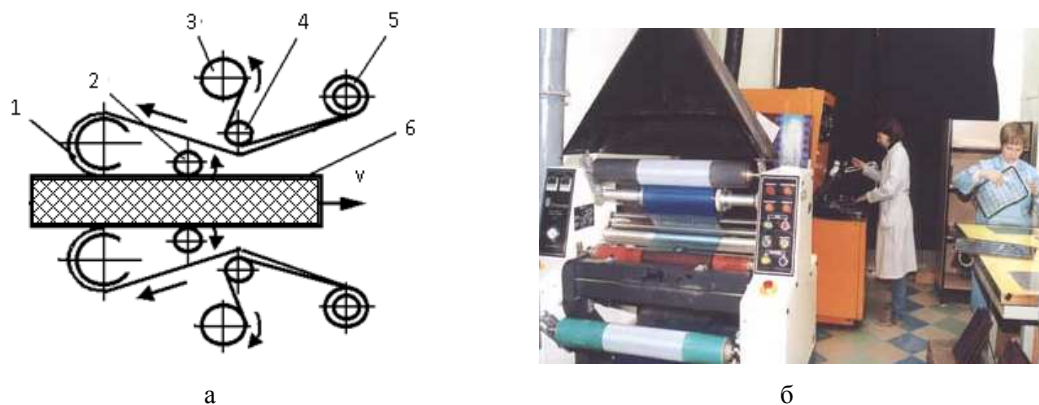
Схема (а) и внешний вид (б) ламинатора
